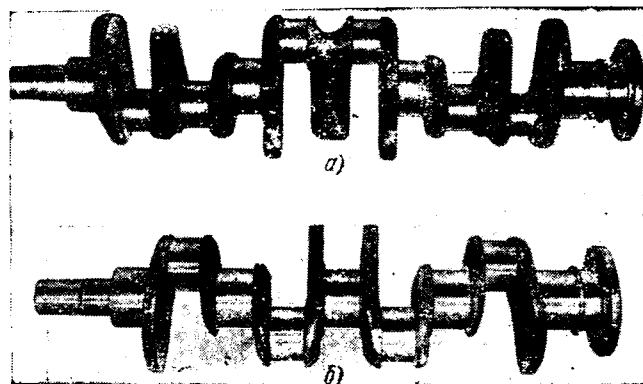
Коленчатые валы двигателя ГАЗ-51 (а) и двигателя М-21 «Волга» (б).
